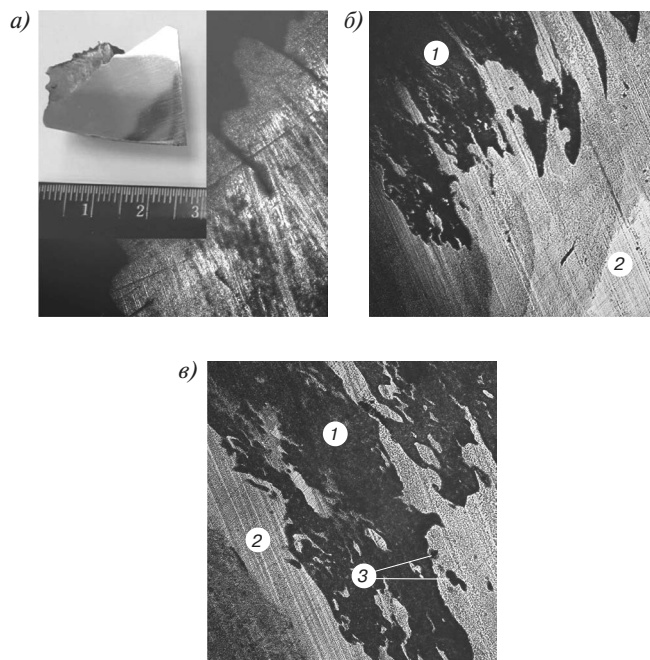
Область электродуговой наплавки на поверхности выпускного клапана: а — наплавленный слой на поверхности клапана; б — граница основного металла и наплавленного слоя; в — граница раздела фаз и дефекты в структуре металла: 1 — наплавленный слой; 2 — основной металл; 3 — шлаковые включения
